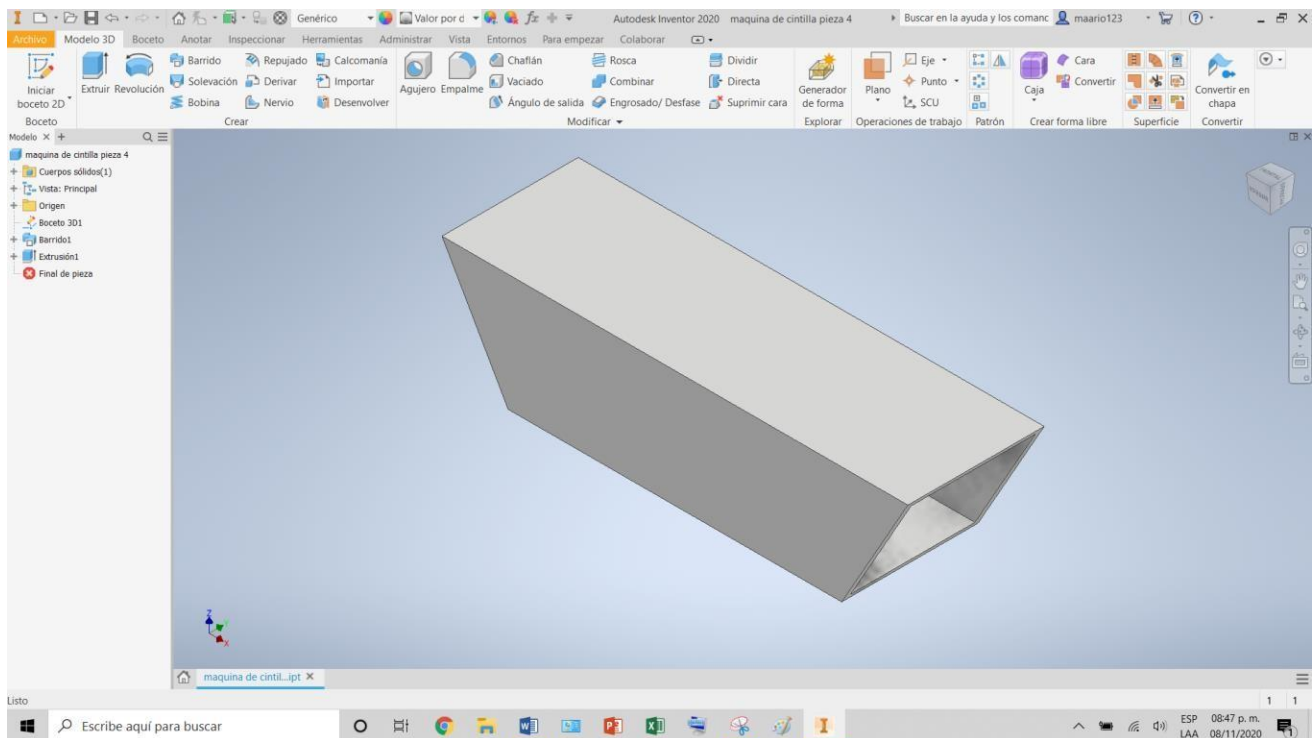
plano de la pieza número tres B para máquina de cintilla.
